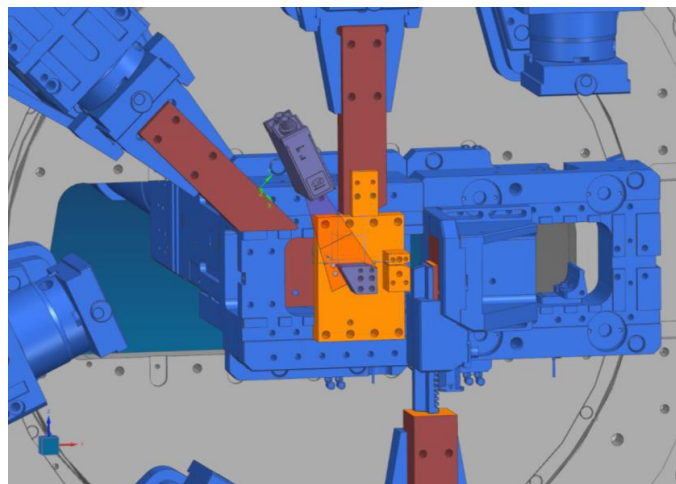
CAD-Darstellung des geplanten Werkzeugs.
